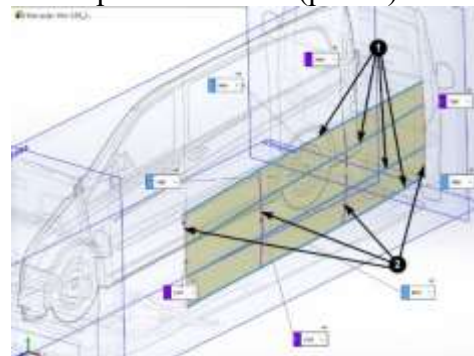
Побудова поверхні бокувни корпусу автомобіля
